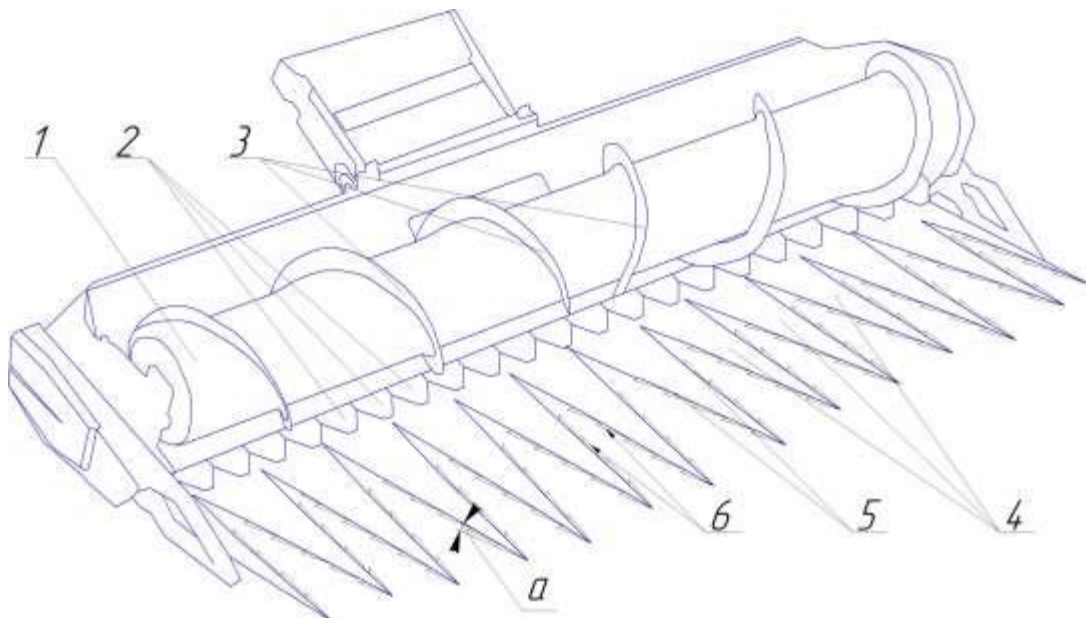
Загальний вигляд жатки зернозбирального комбайна[19].
